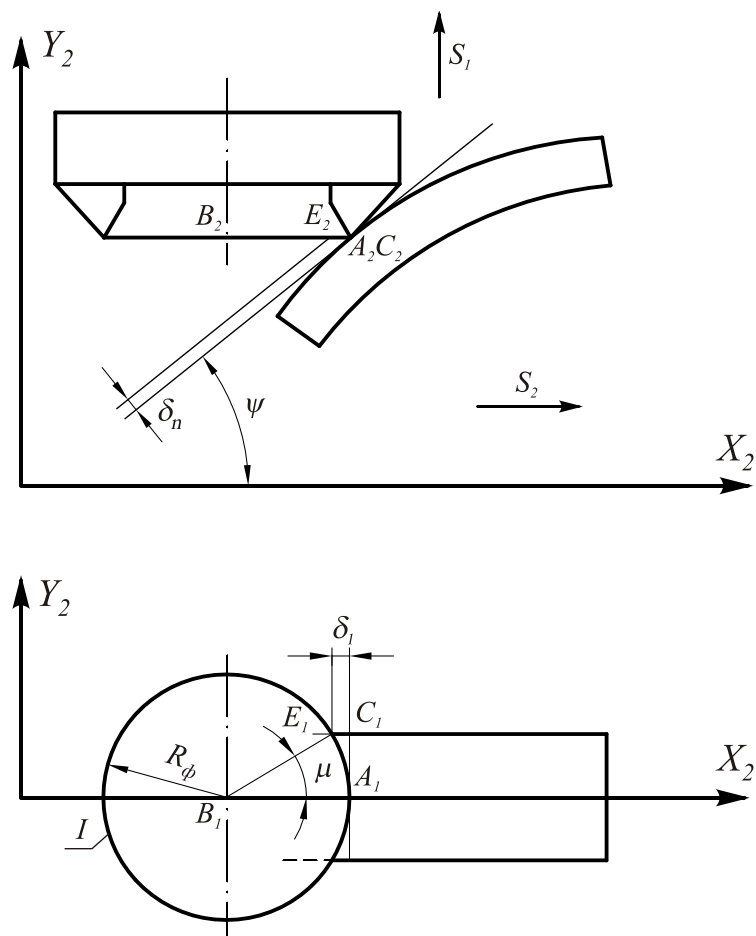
Схема обробки циліндричної поверхні торцевою фрезою з прямолінійними кромками
